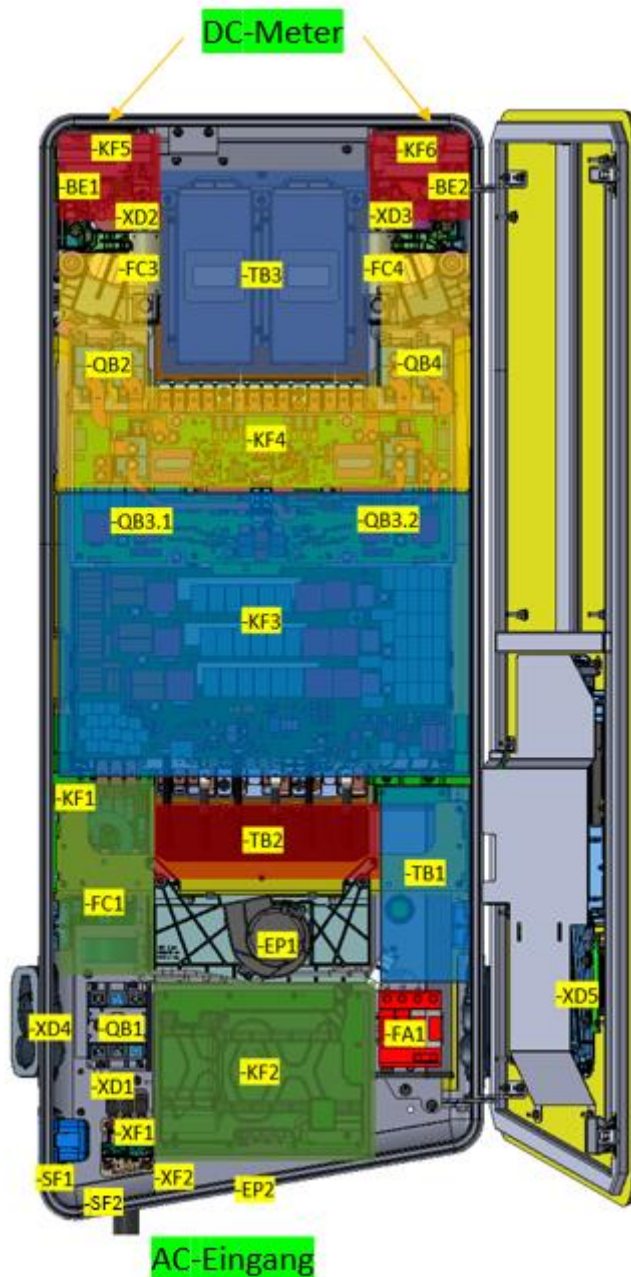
Innenansicht HYC50 (frontale Ansicht)
